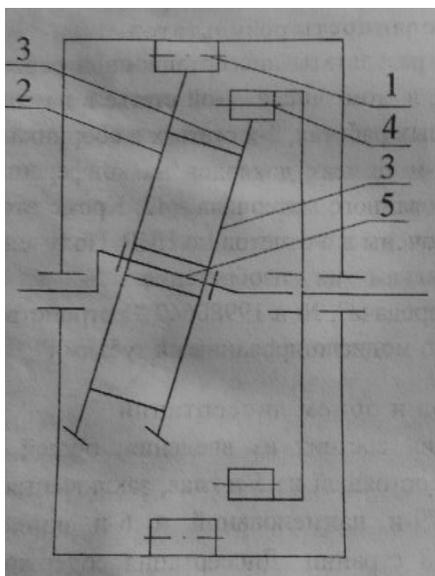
Кинематическая схема ППП: 1- неподвижное центральное колесо; 2- венец 3- венец; 4- подвижное центральное колесо; 5- кривошип
